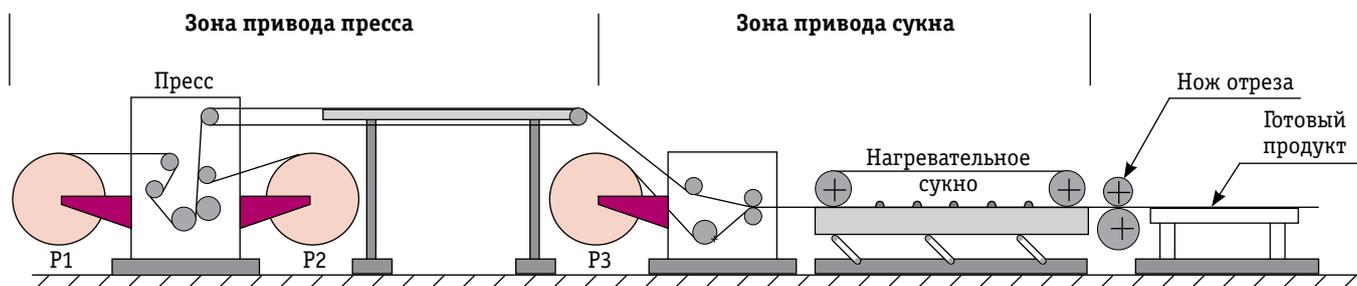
Кинематическая схема гофроагрегата ЛИГ-105/20Э
